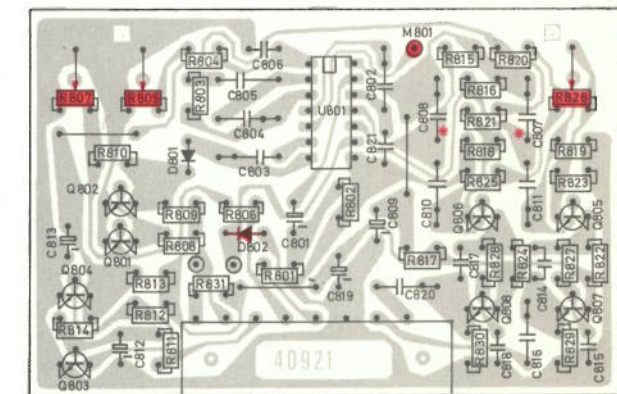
Plate (1. utgave) for stereodekoder 5-3 (sett fra loddessiden), brukt på en del Huldra 10 mottakere
